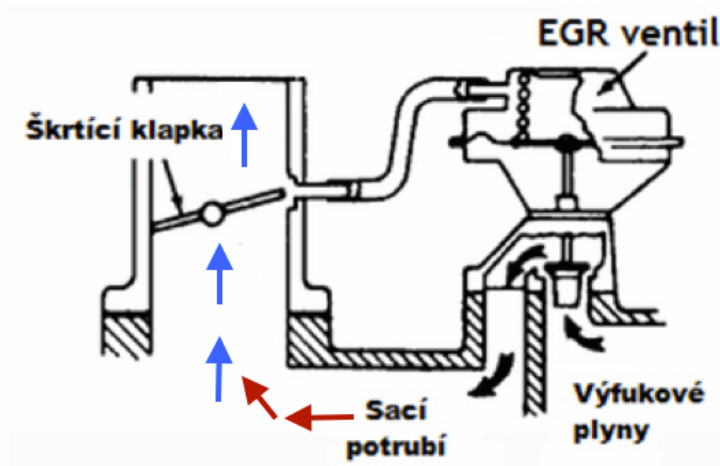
Princíp funkcie EGR technológie vznetrového motoru [2]
